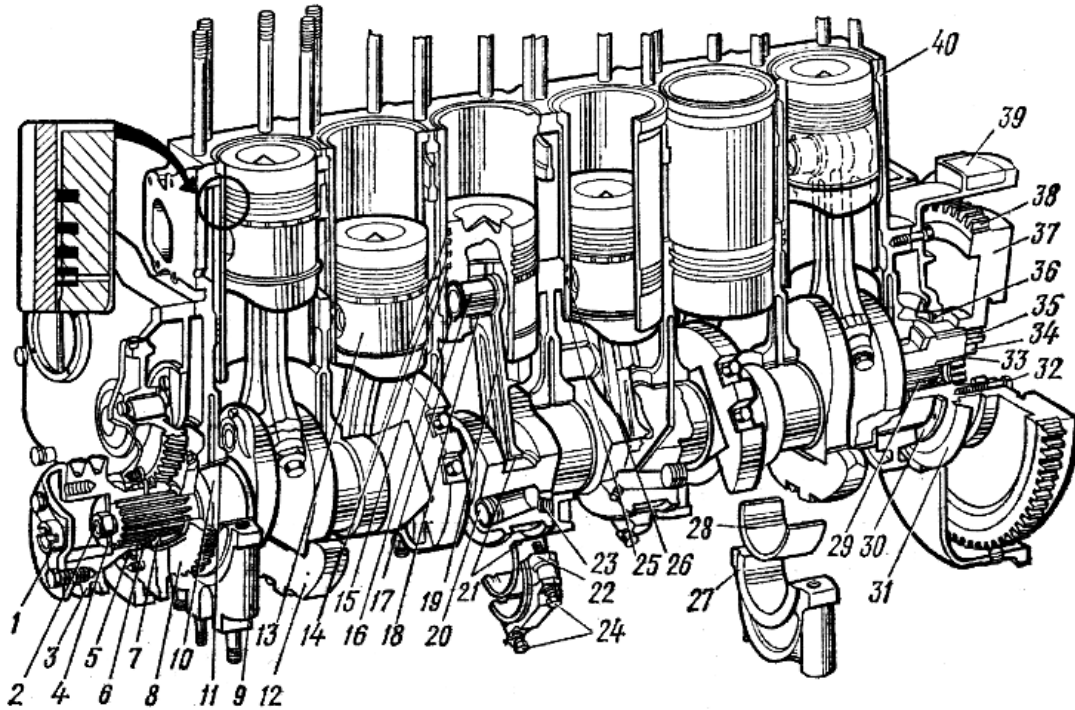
Кривошипно-шатунный механизм двигателя А-01М:
